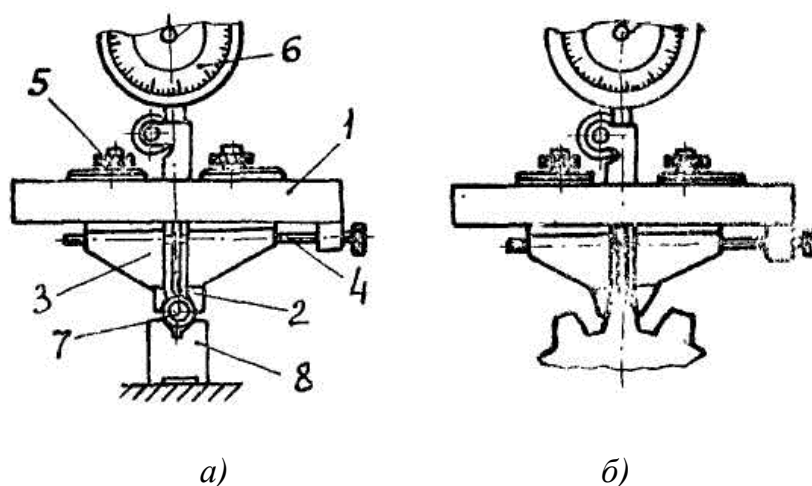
Тангенциальный зубомер: а – схема настройки прибора; б – схема измерения прибором
